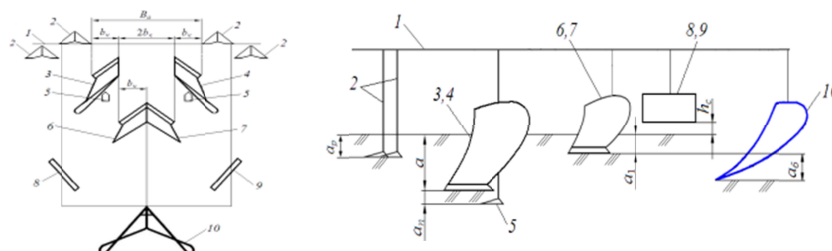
Почвообрабатывающее орудие, вид сверху и сбоку
